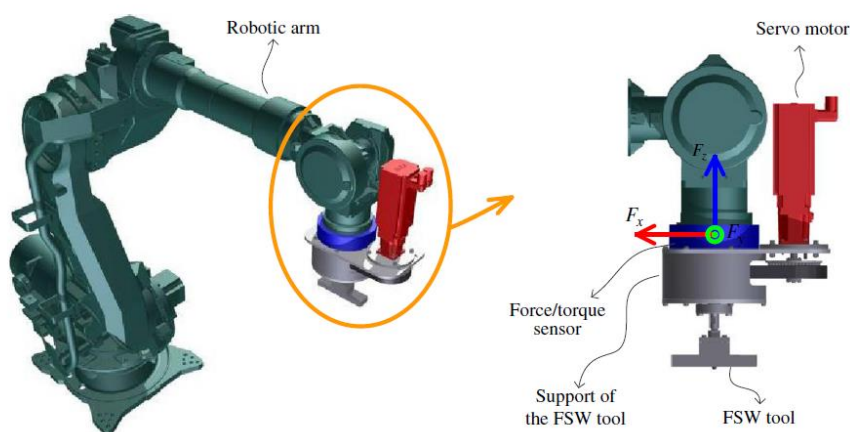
Soldadura por Fricção Linear utilizando a plataforma Robótica (Mendes, 2014).
